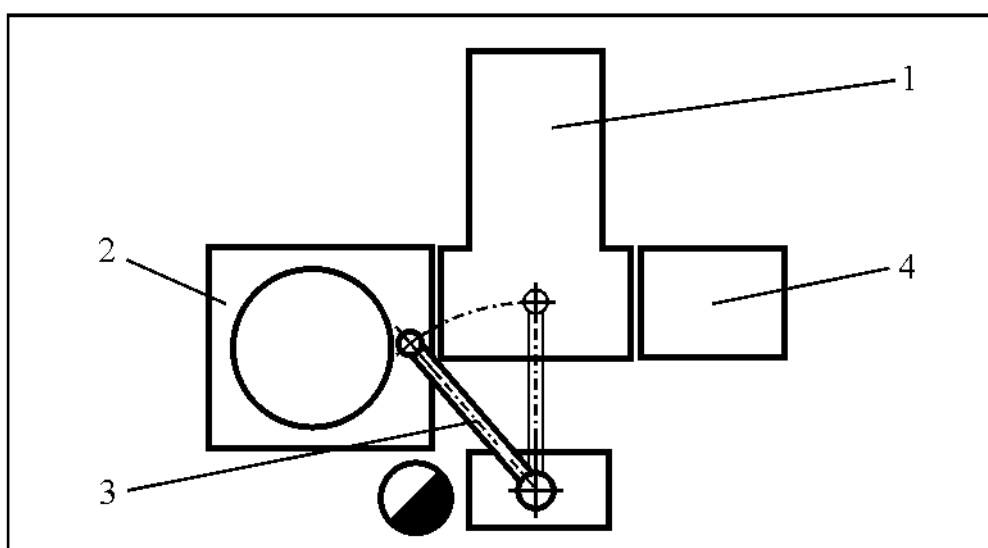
План-схема організації робочого місця оператора, що обслуговує роботизований штампувальний комплекс для роботи від штучної заготовки: 1 - кривошипний відкритий прес; 2 - автоматизований бункерний завантажувально-орієнтовочний пристрій; 3 - маніпулятор; 4 - бункер для деталей
